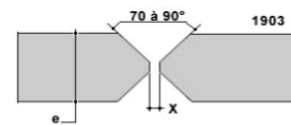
Classification par type de soudage (Soudage TIG)
